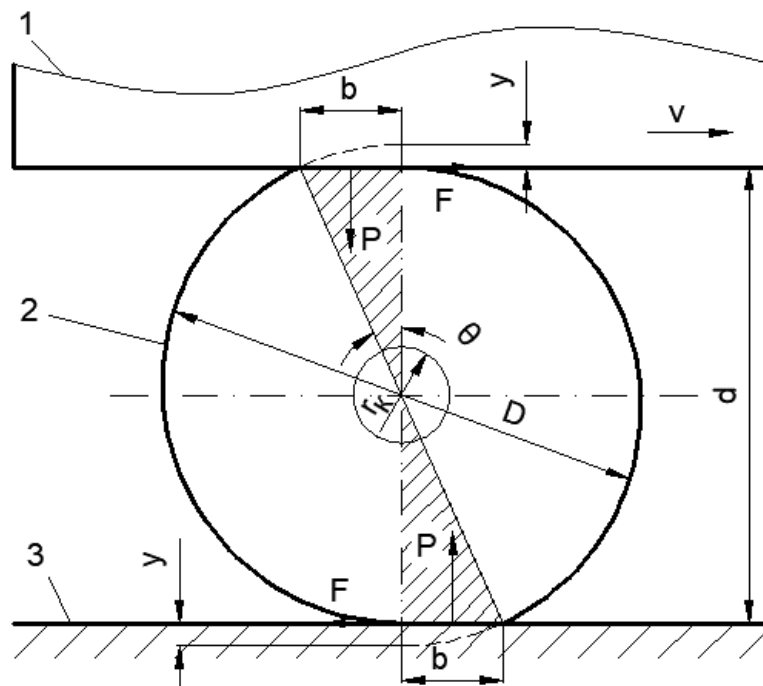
Схема усилий при поперечной обкатке плоскими плитами: 1 – подвижная плита; 2 – заготовка; 3 – неподвижная плита; r_k – радиус упругого ядра
